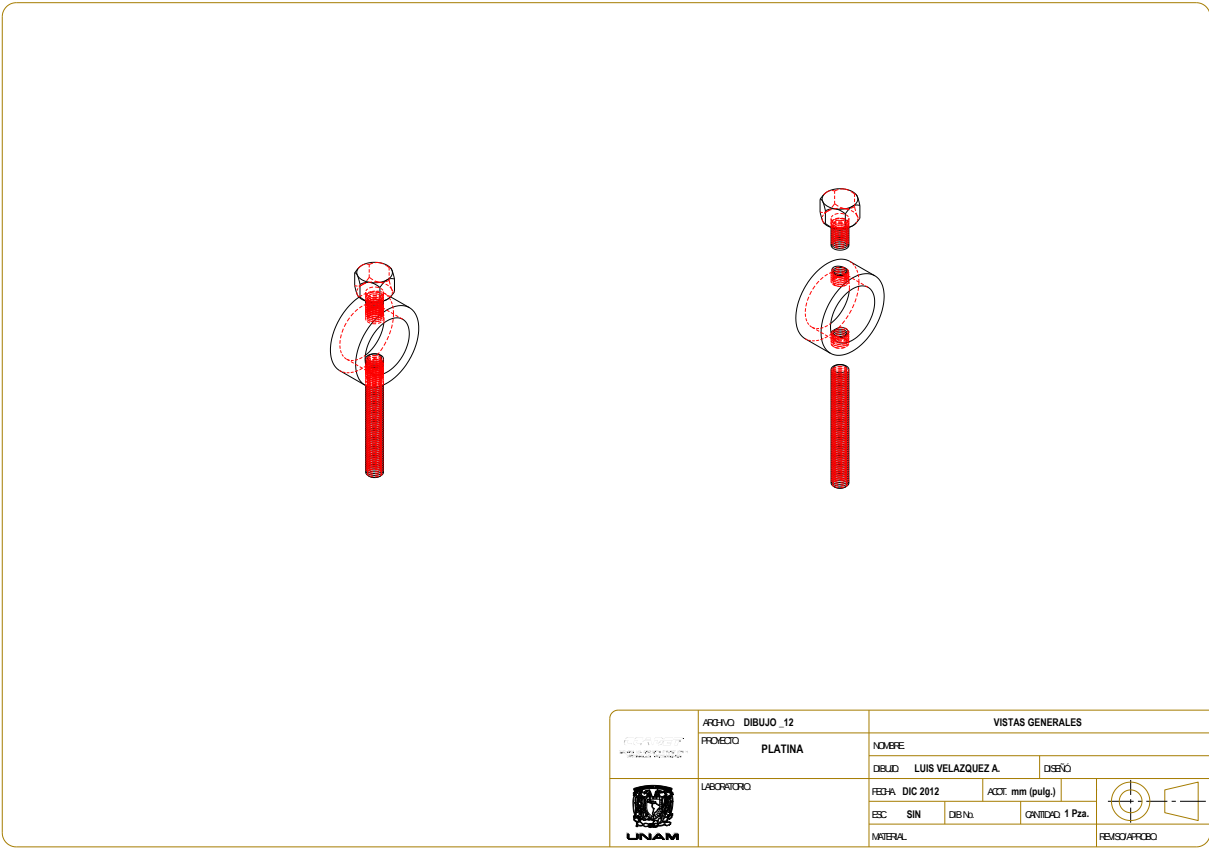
Ensamble y explosivo del soporte anular del LED.
